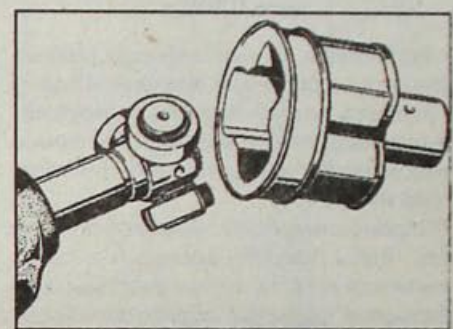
Снятие корпуса шарнира равных угловых скоростей
